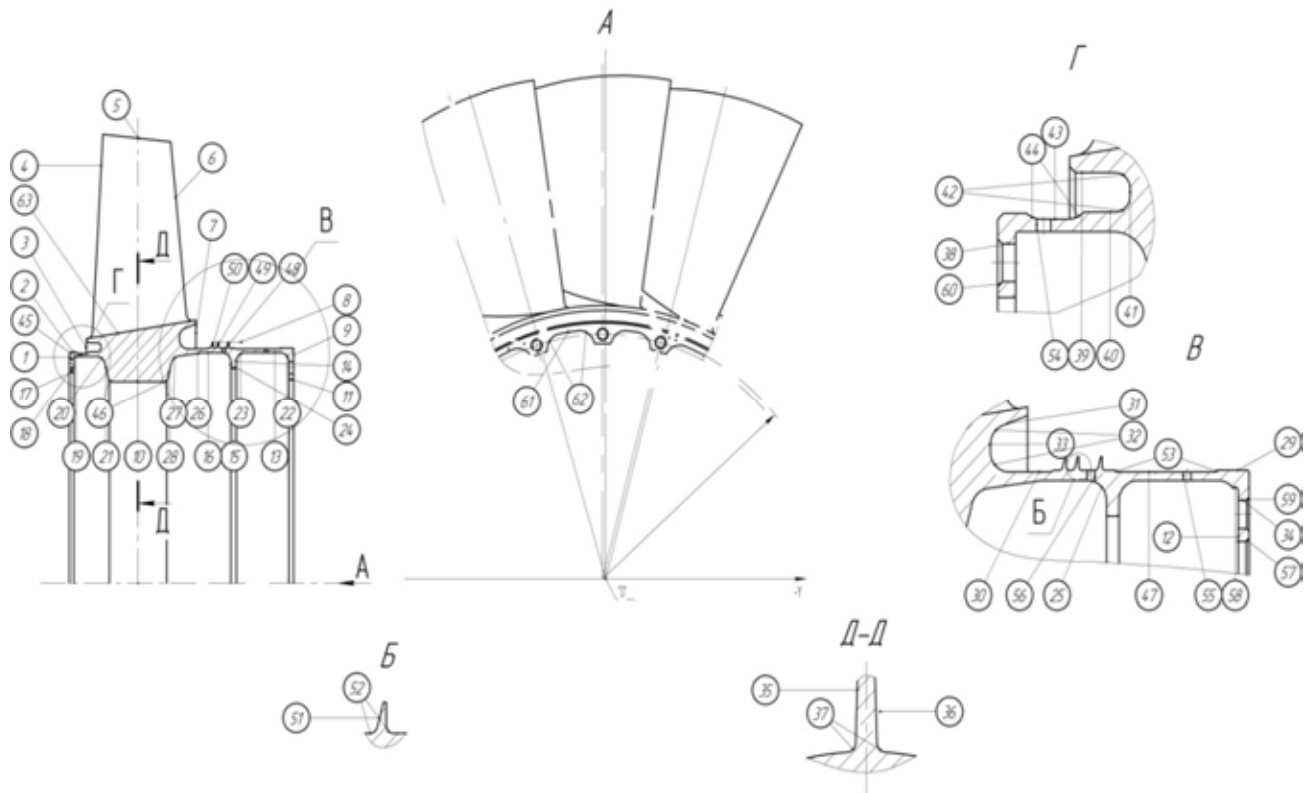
Ескіз моноколеса з нумерацією поверхонь
